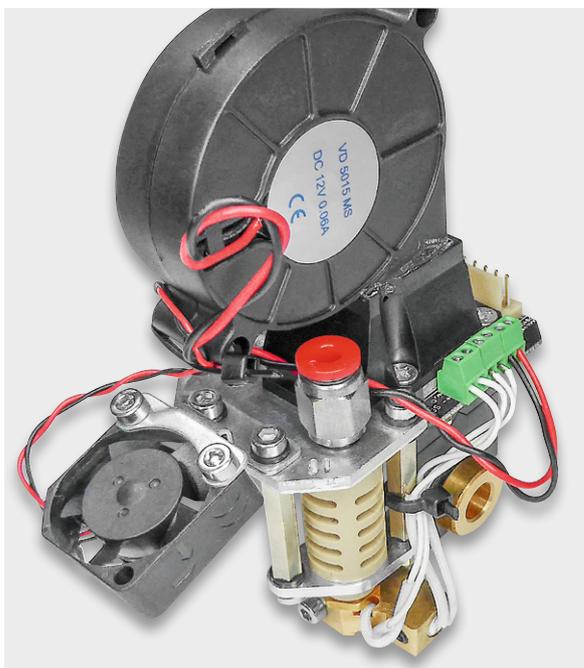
Der fertig montierte Druckkopf mit Lüftern und Filamentzuführung
